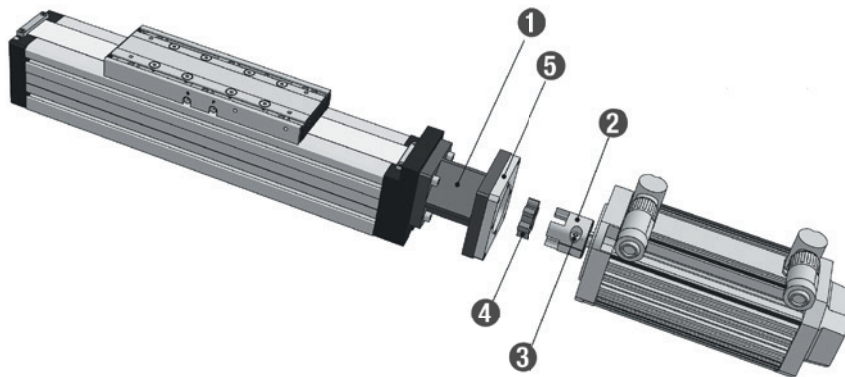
Motormontage an Linearachsen mit Spindeltrieb und Kupplungsglocke
